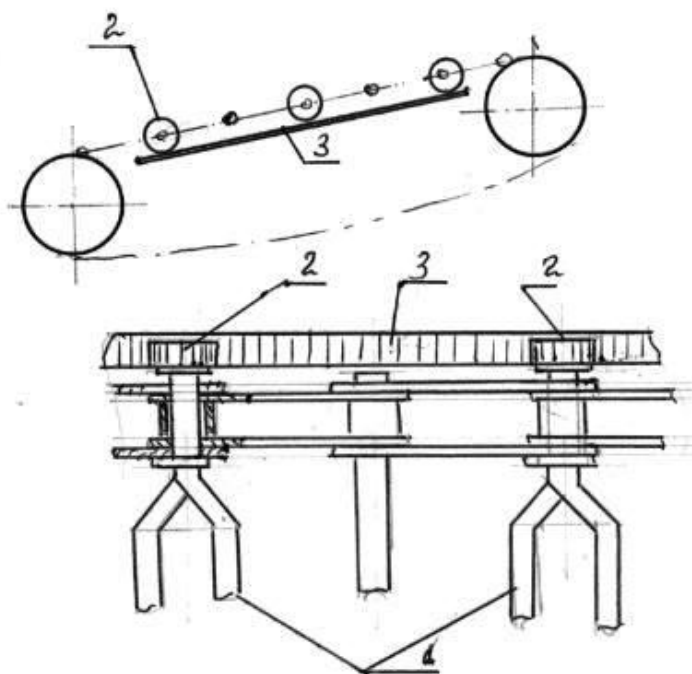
Схема элеватора с вращающимися рамками и неподвижной рейкой:
